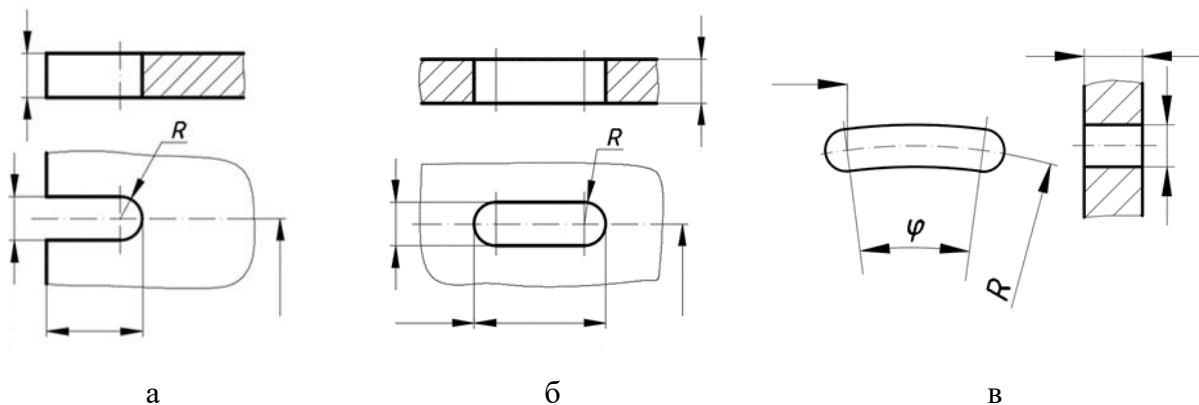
Образец выполнения пазов и продолговатых отверстий.
